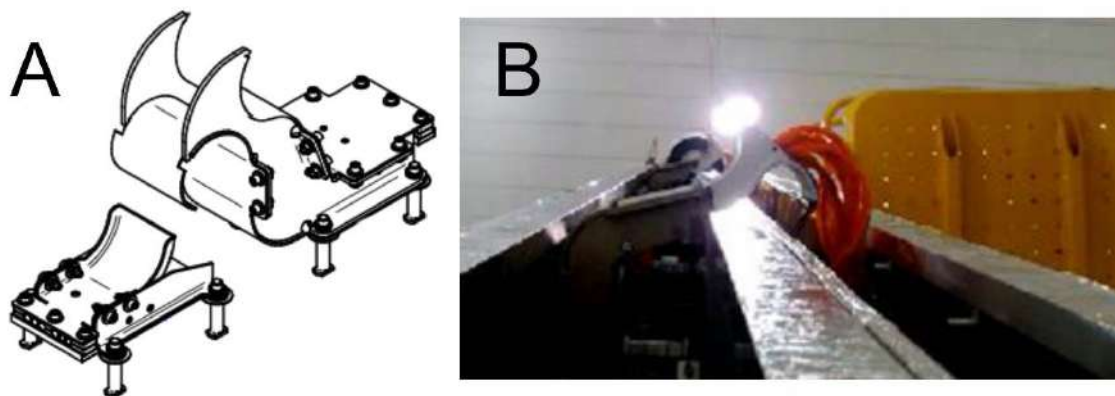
A: Esquema de un soporte guía de cables; B: Vista de un soporte guía de cables.
